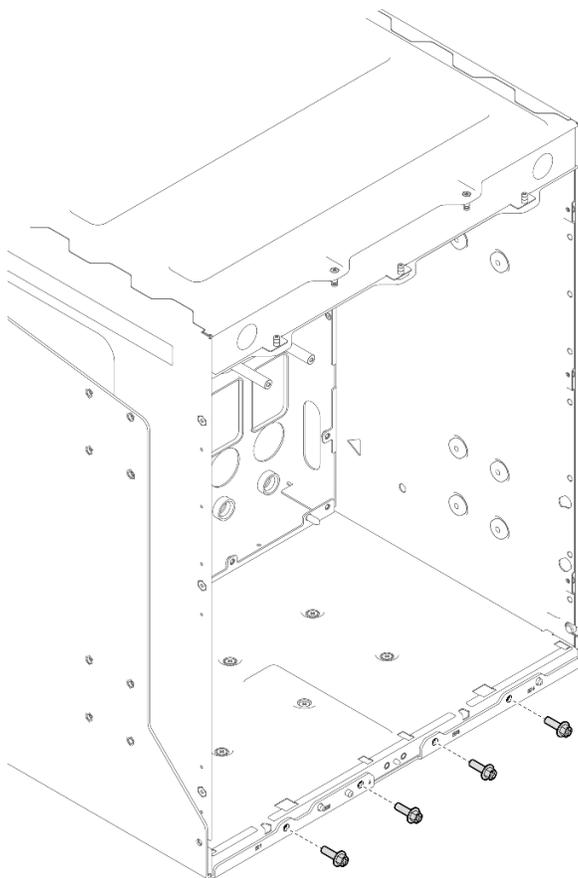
Fixation du support arrière à l'extrémité arrière du boîtier
